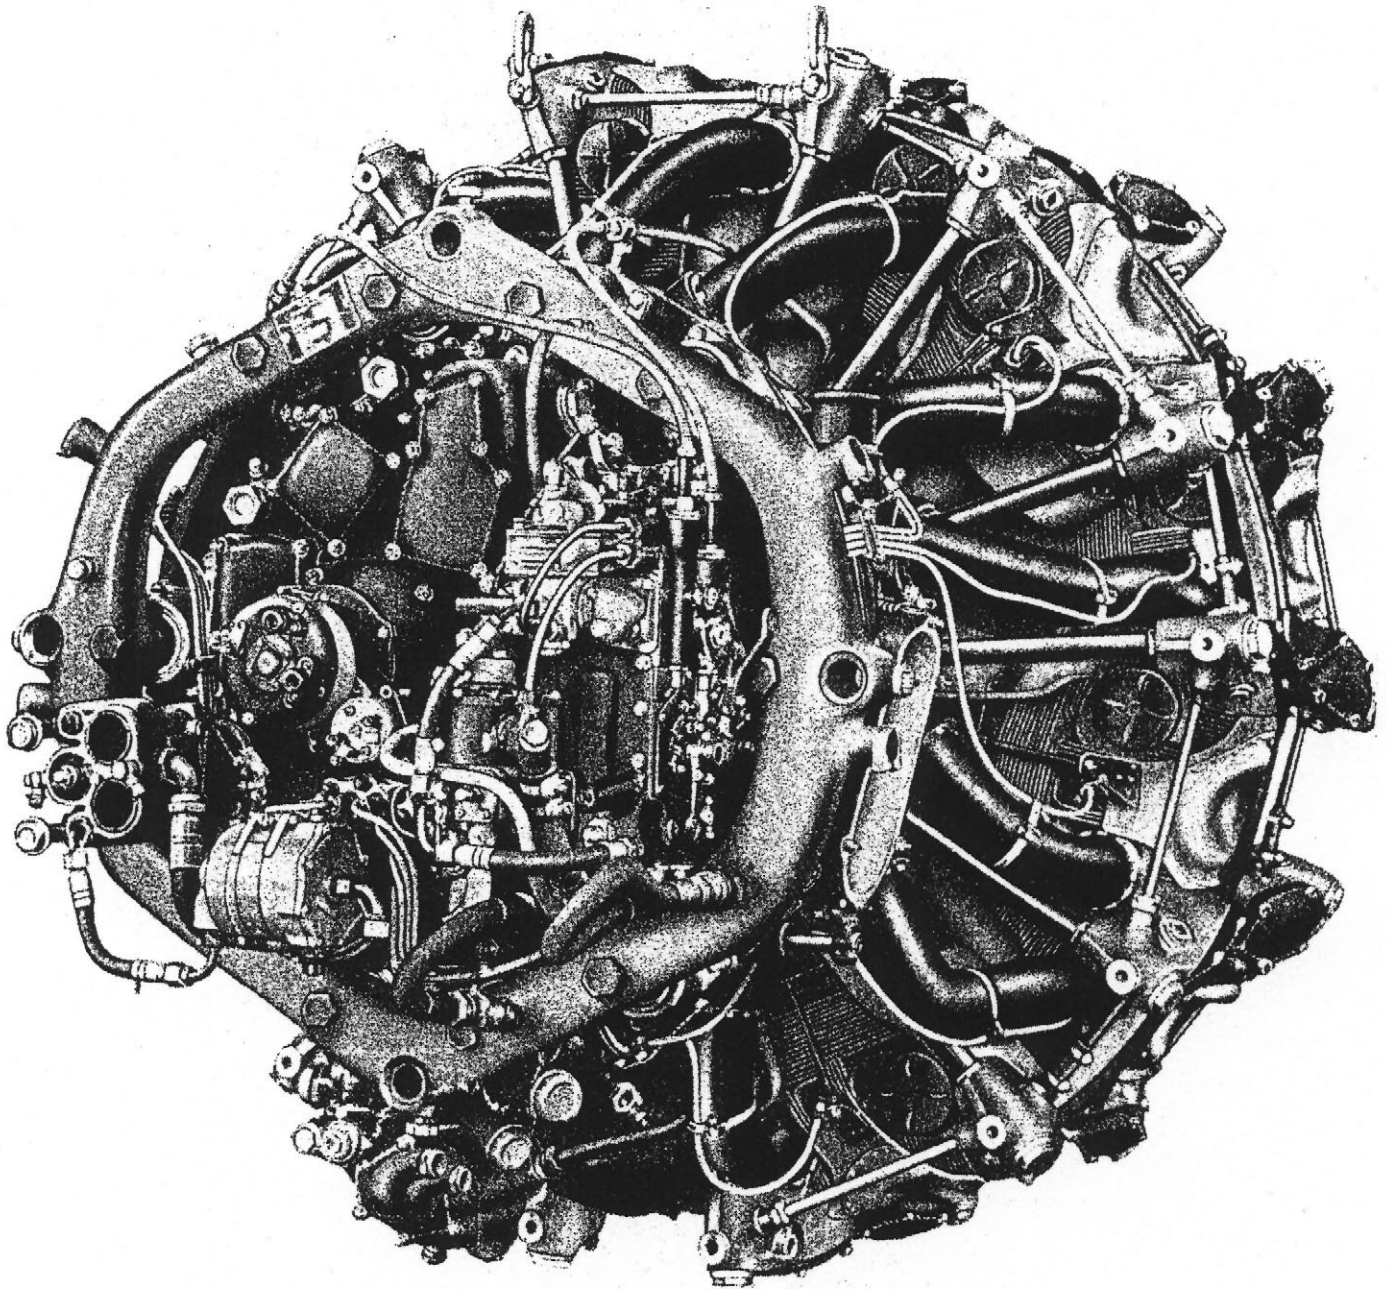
Motor BMW 801 C u. BMW 801 D, Ansicht halbrechts von hinten
